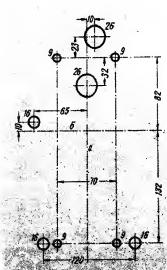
Сверление отверстий для установки на изоляционных панелях контакторов типа КП 504 и КП 514 с задним присоединением
